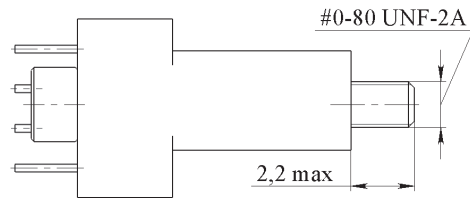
Соединитель СП450-03...2...Ш1...
